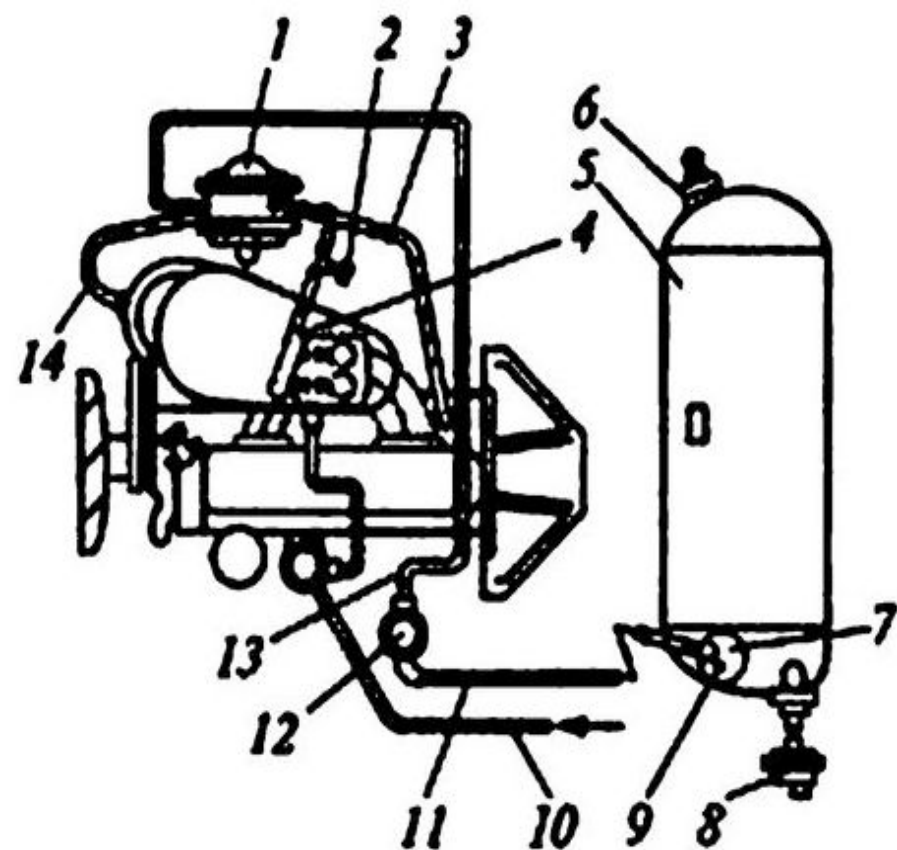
Схема газобаллонной установки для работы на СНГ автомобиля ГАЗ-24-17 «Волга»:
